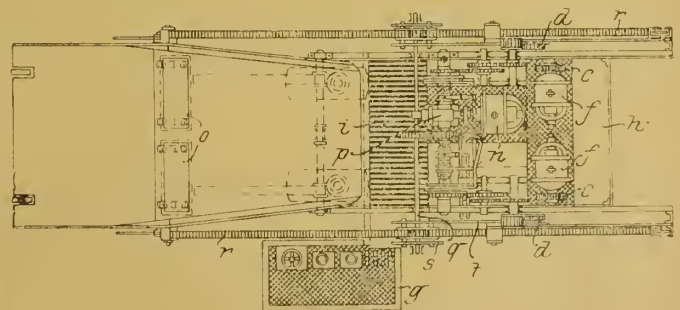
Grundriß der Schaufelvorrichtung von Clausen.
